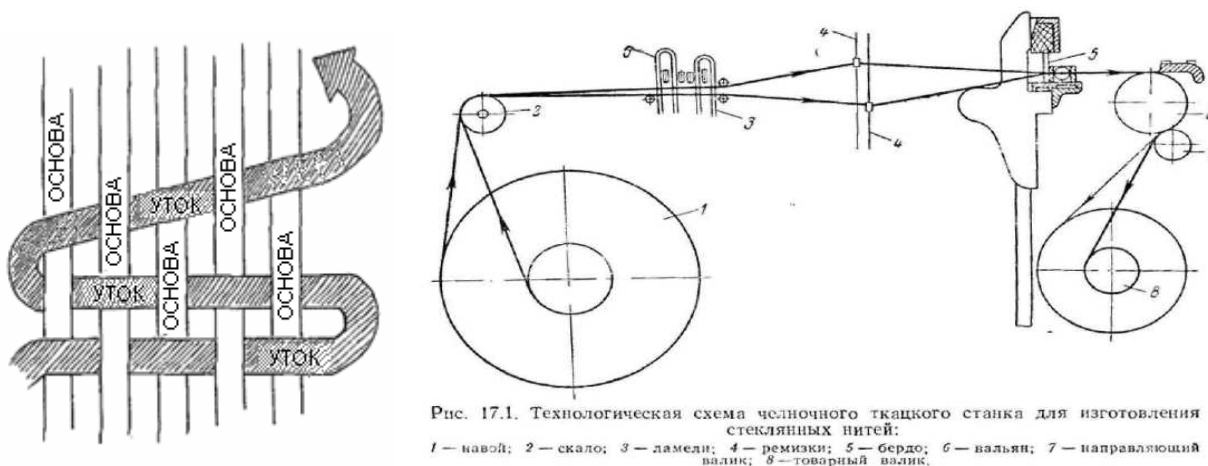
Технологическая схема челночного ткацкого станка. 1 – навой; 2 - скало; 3 - ламели; 4 - ремизки; 5 - бердо; 6 - вальян; 7 – направляющий валик; 8 – товарный валик.
